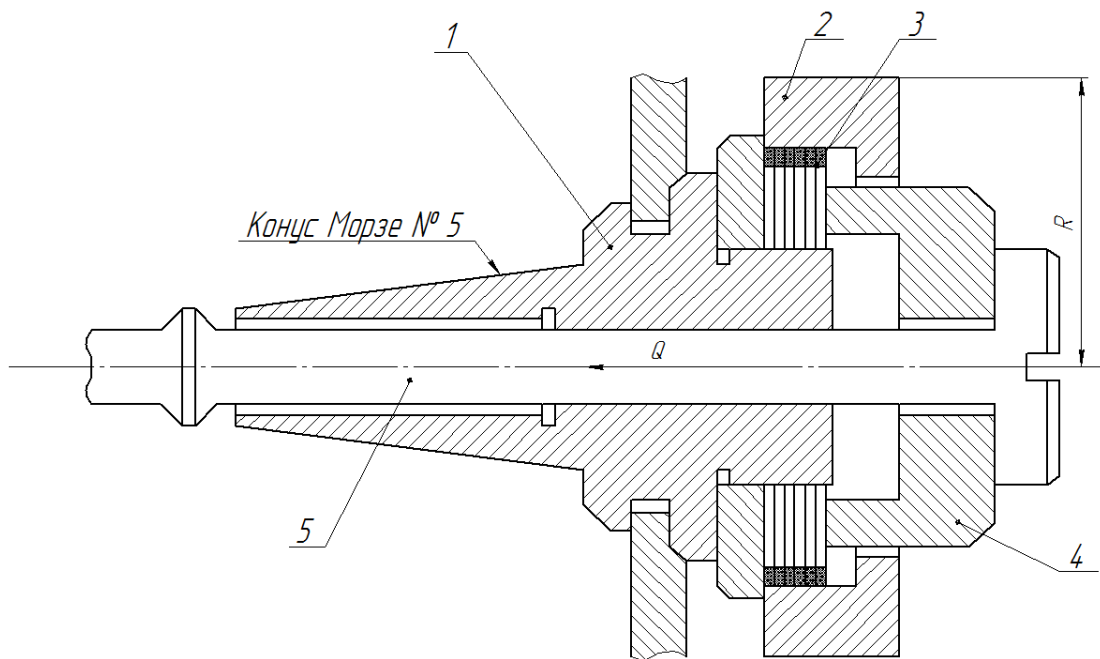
Будова й параметри консольної оправки з тарілчастими пружинами: 1 – оправка; 2 – заготівка; 3 – пакет тарілчастих пружин; 4 – втулка; 5 – механічний привід; R – радіус оброблюваної поверхні заготівки; Q – осьова сила на штоку механізованого приводу
